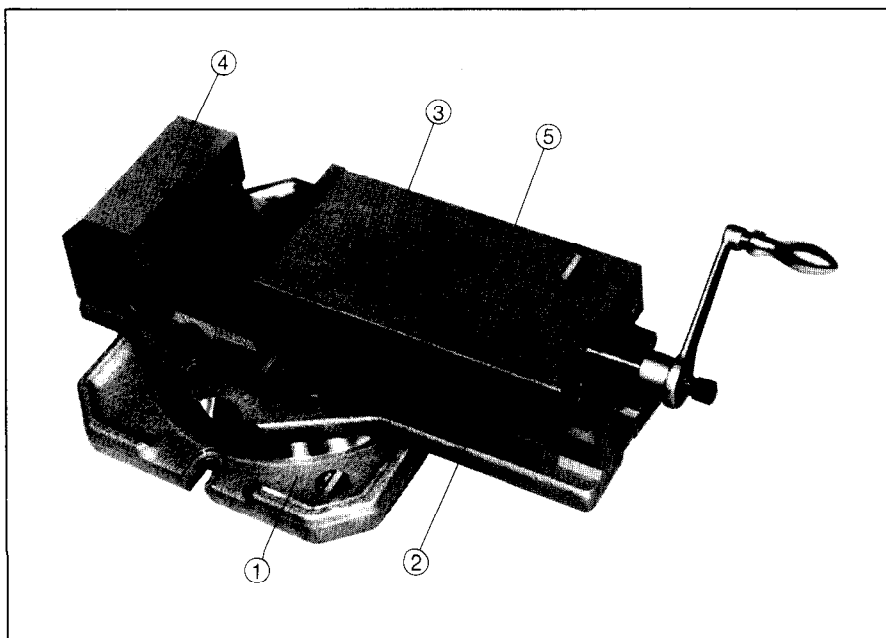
Gesenkgeschmiedete Teile eines Hydro-Maschinenschraubstockes:
